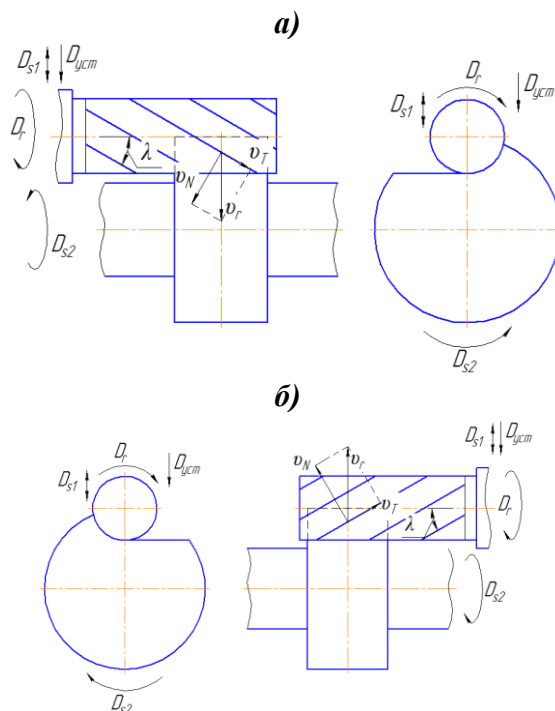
Схемы обработки плоской поверхности детали при попутном (а) и встречном (б) фрезеровании
